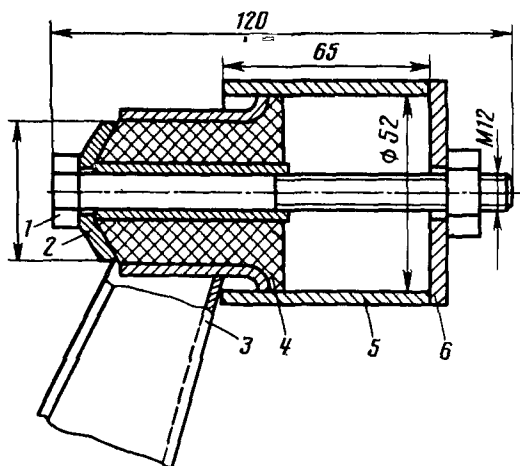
Выпрессовка сайлент-блока из рычага балки задней подвески:
